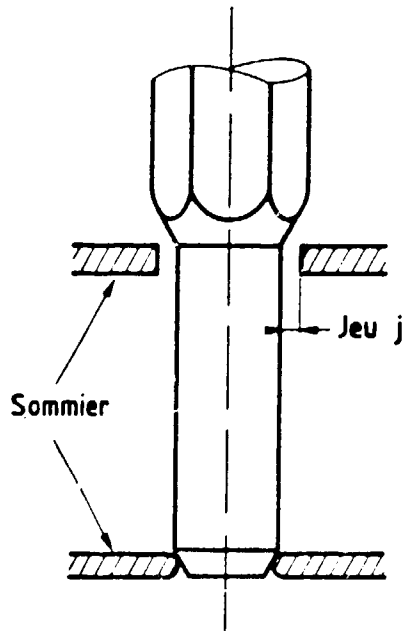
LIAISON ASSEMBLAGE COMBUSTIBLE-SOMMIER
